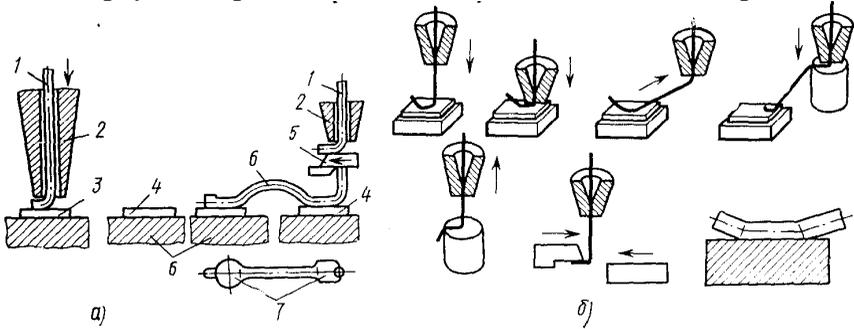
Последовательность переходов при термокомпрессионной сварке без образования шарика
